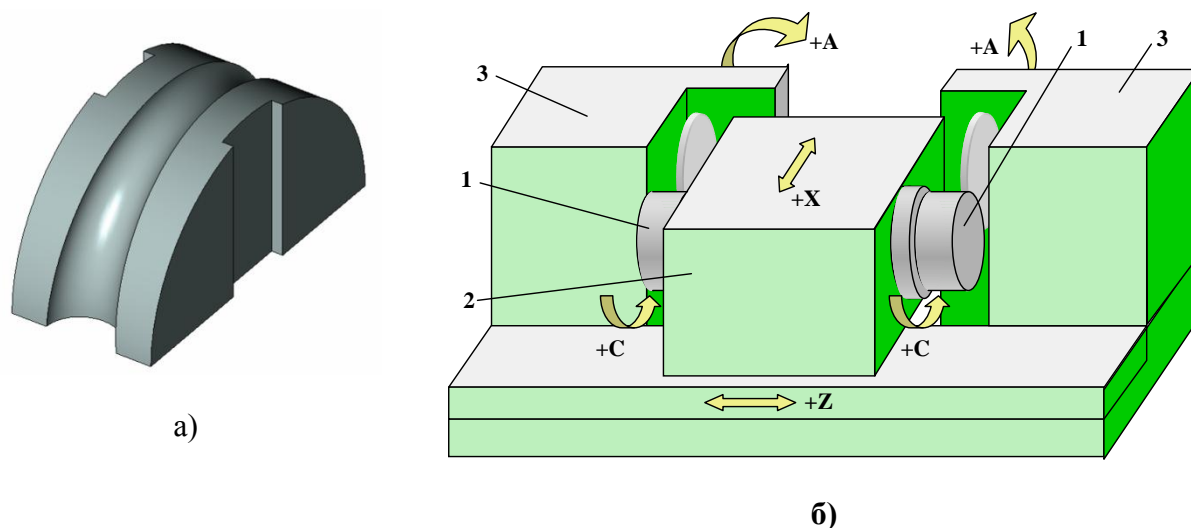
Калибр холодной прокатки (а) и схема станка для его изготовления (б)
